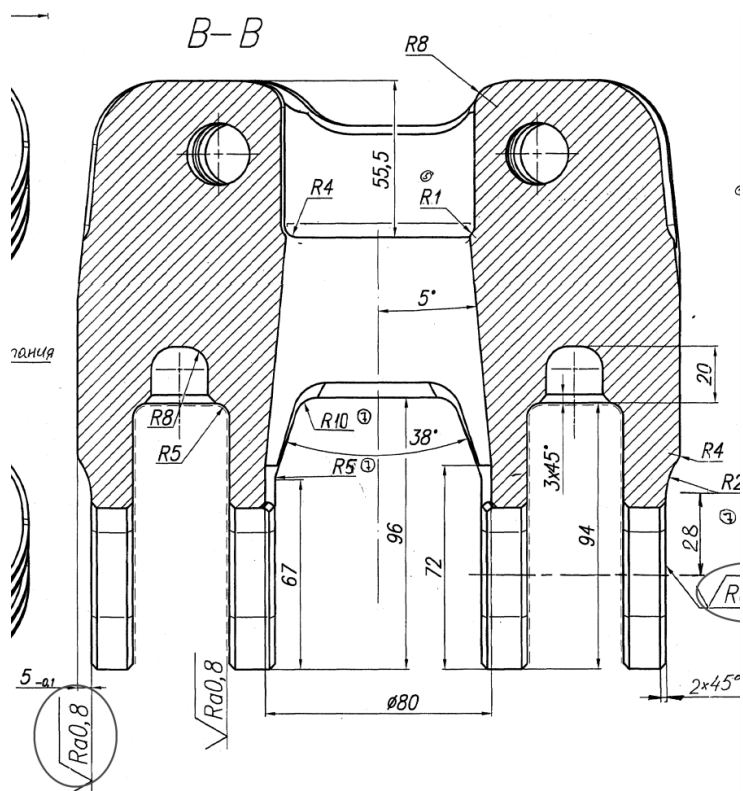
Шероховатость поверхностей $Ra0,8$
